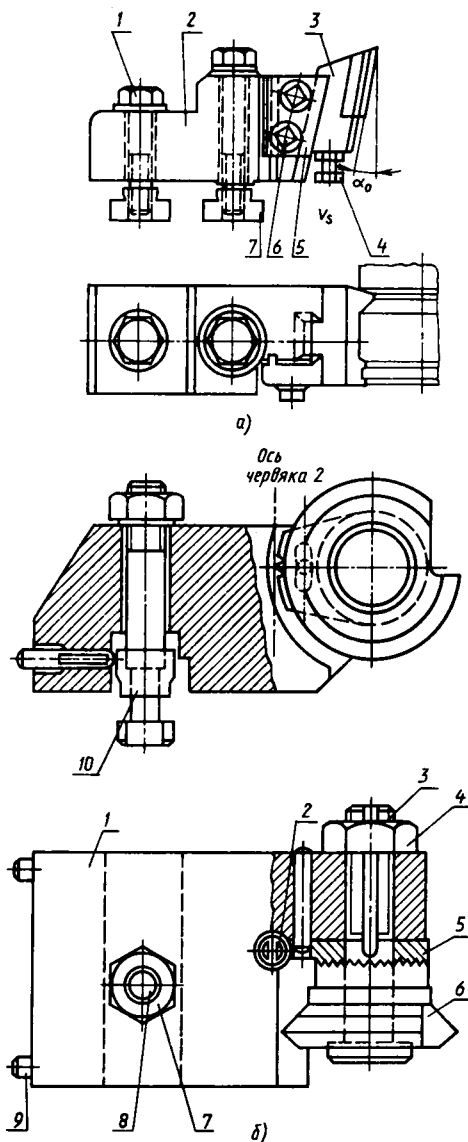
Резцедержатели для крепления фасонных резцов:
